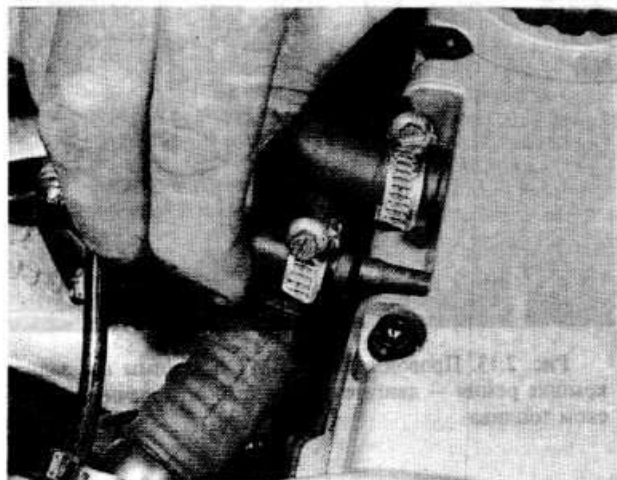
Снятие шланга с задней крышки распределительного механизма — двигателя с двумя распредвалами
